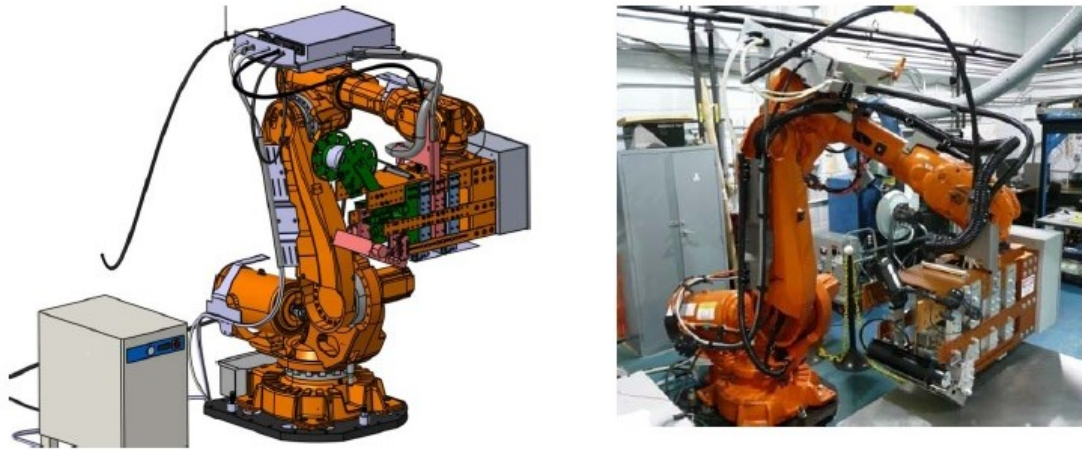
Modularer TLK des CCM, links: Darstellung im CAD System, rechts: Aufbau im realen Umfeld [12].
